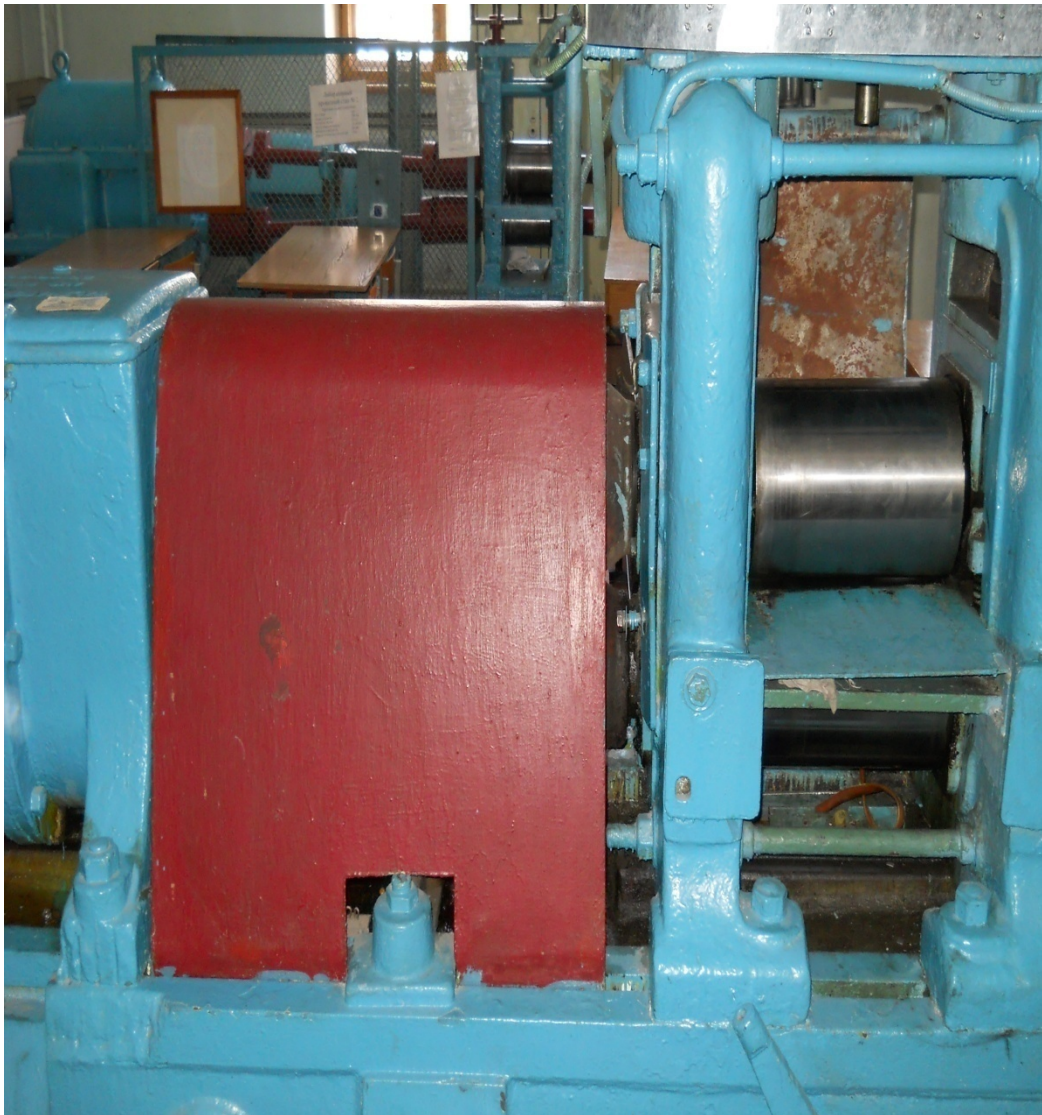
Загальний вид устаткування лабораторного прокатного міні-стану 260x260.
